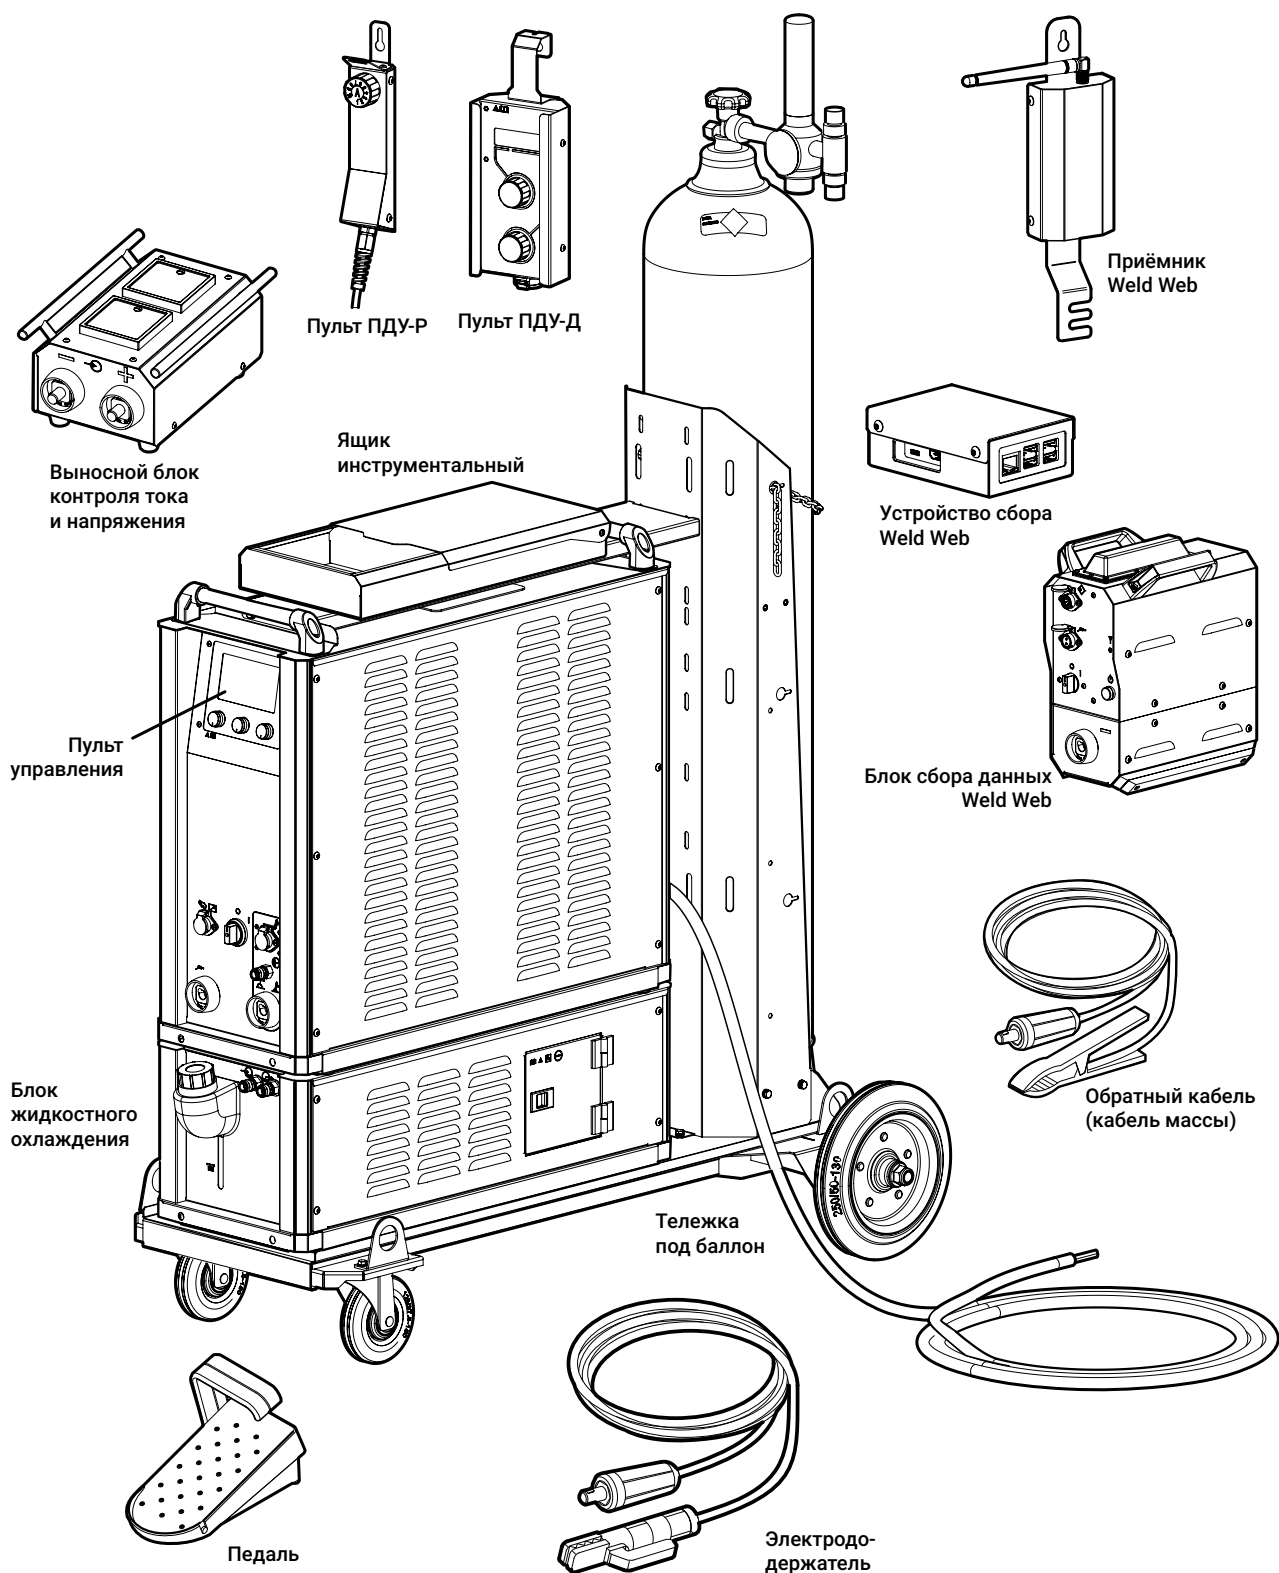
Общий вид некоторых составных частей и аксессуаров для сварочного аппарата для аргонодуговой сварки. Внешний вид может отличаться от представленного
